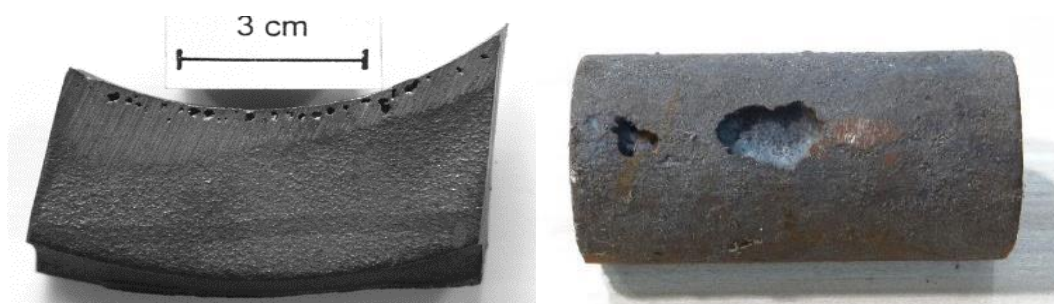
Defeito de bolhas de gás (esquerda) e explosão (direita)
